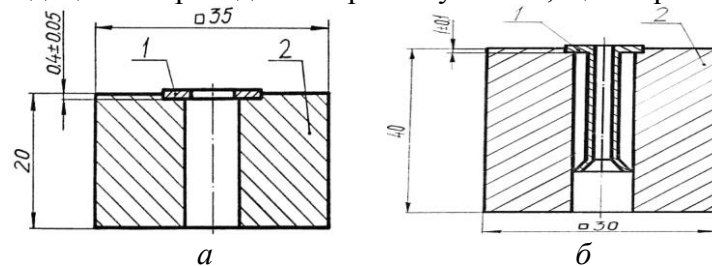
Пристосування для механічного оброблення поверхонь: а – для алюмінієвої прокладки; б – для мідного анода; 1 – деталь, що обробляється, 2 – пристосування
